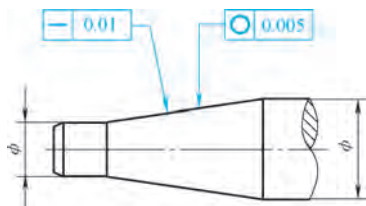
同一要素有多项几何公差要求时的标注
